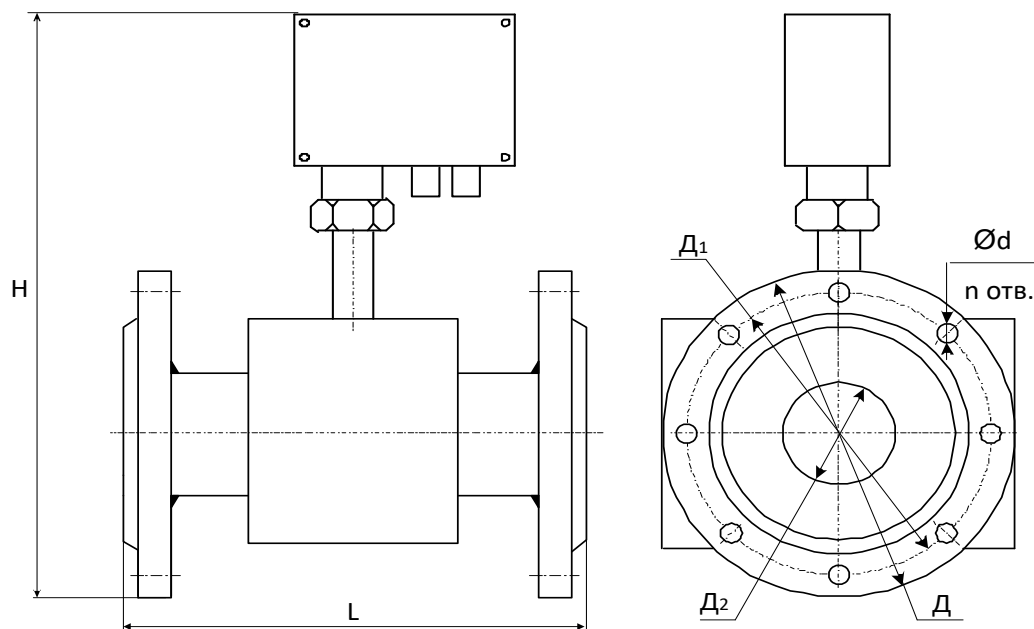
Габаритные и присоединительные размеры, преобразователей с фланцами
